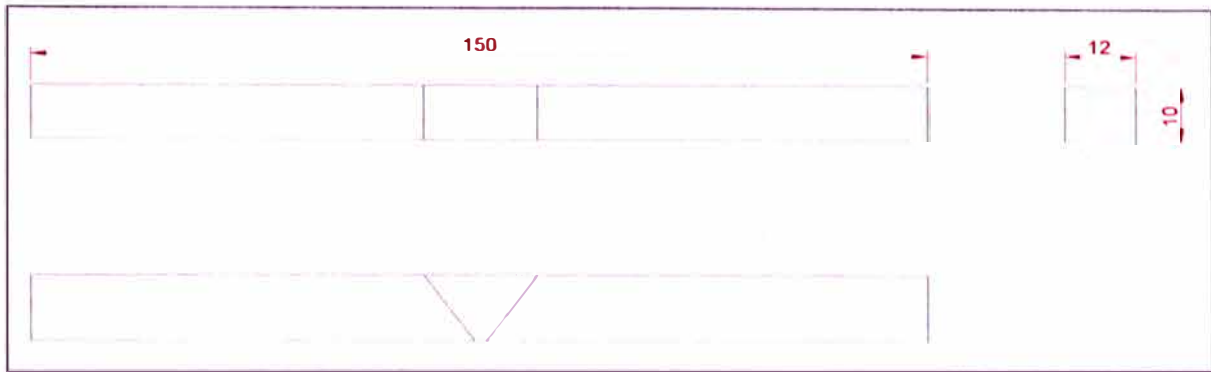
Dimensión de probeta para ensayo de doblado de lado.
